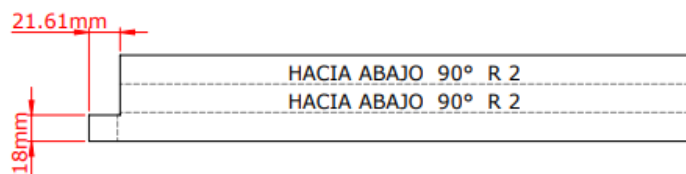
Sección 2 de la puerta - Plancha desplegada
